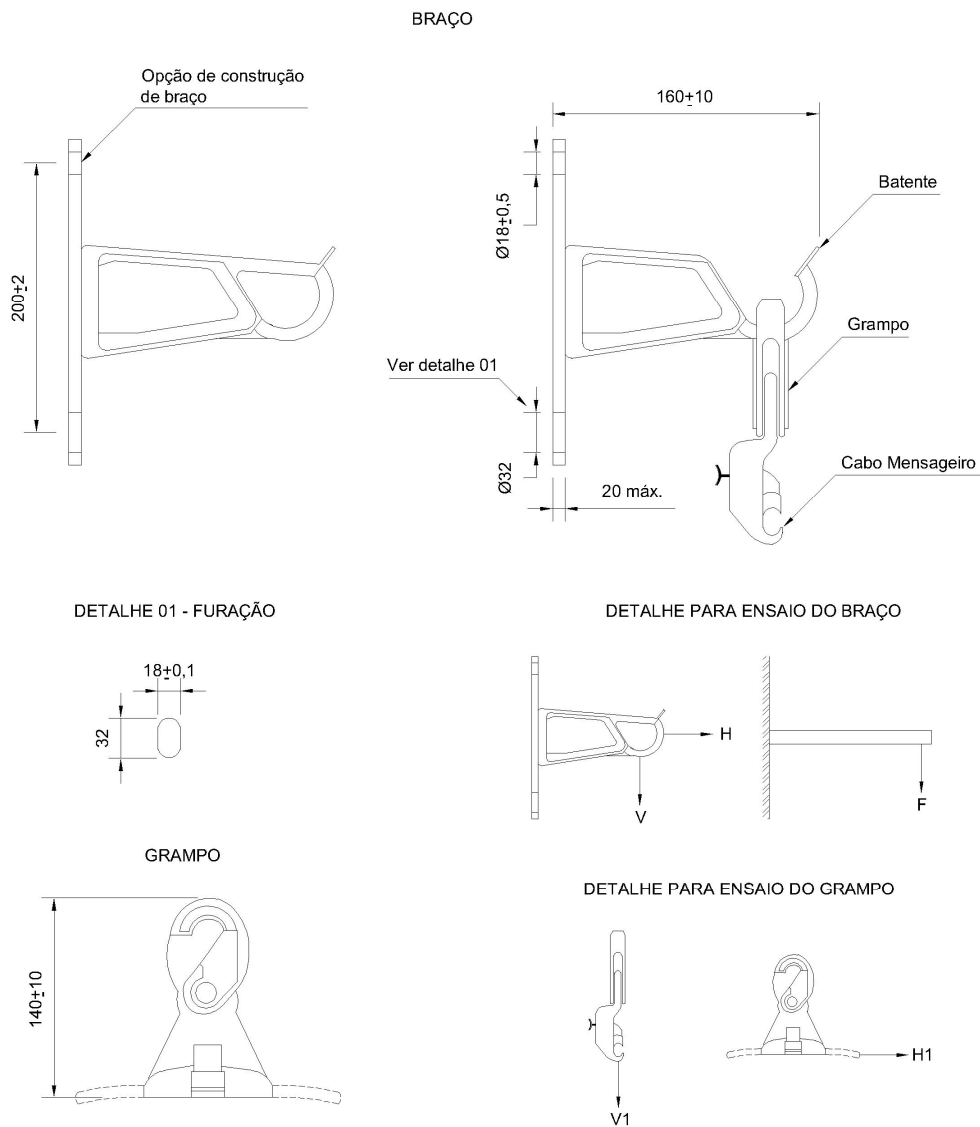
Desenho dimensional conjunto grampo de suspensão
